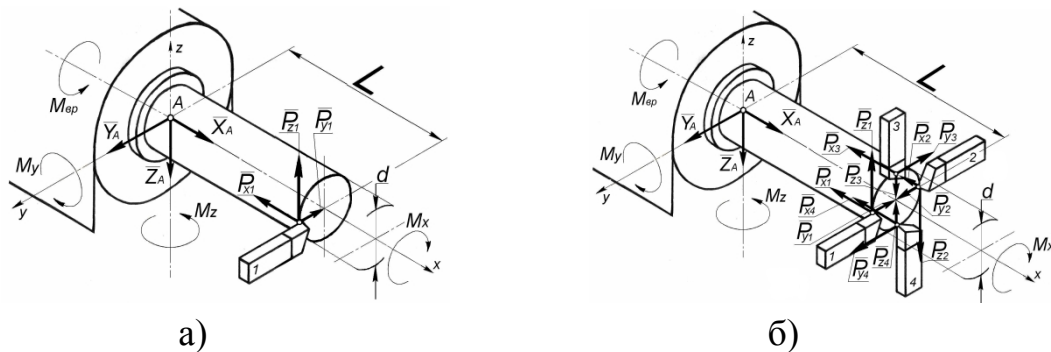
а) обробка заготовки одним різцем; б) обробка заготовки чотирма різцями.
